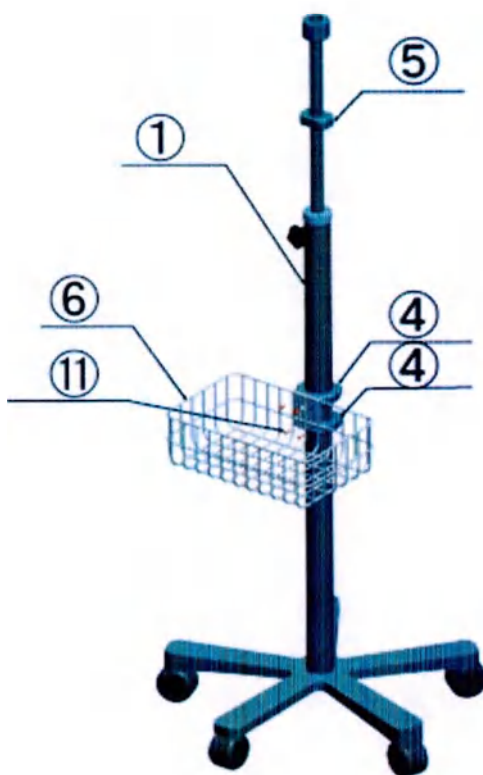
Сборка медицинской стойки Endostand Шаг 3
